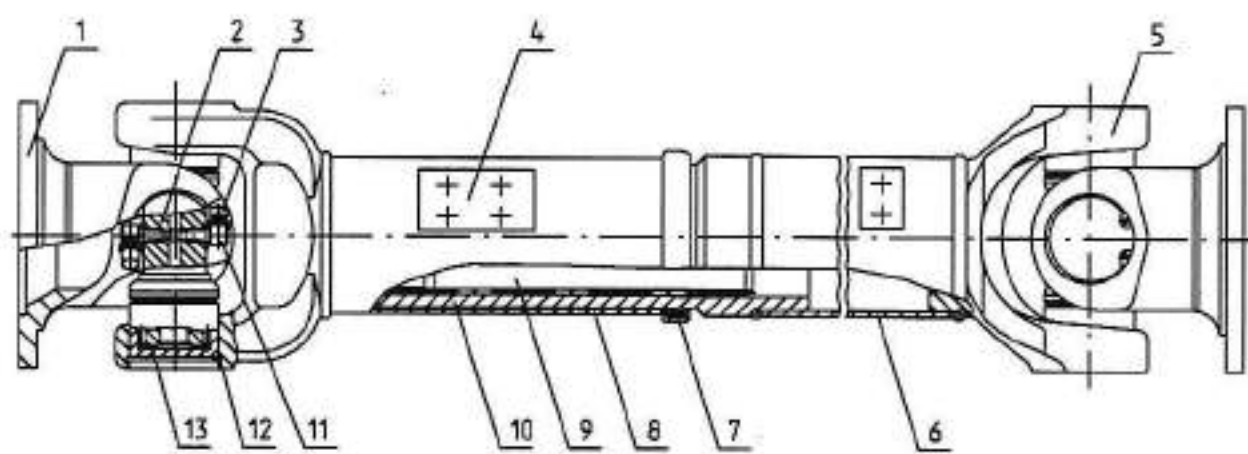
Карданный вал ЖД1-4250010-06 шестой серии:
